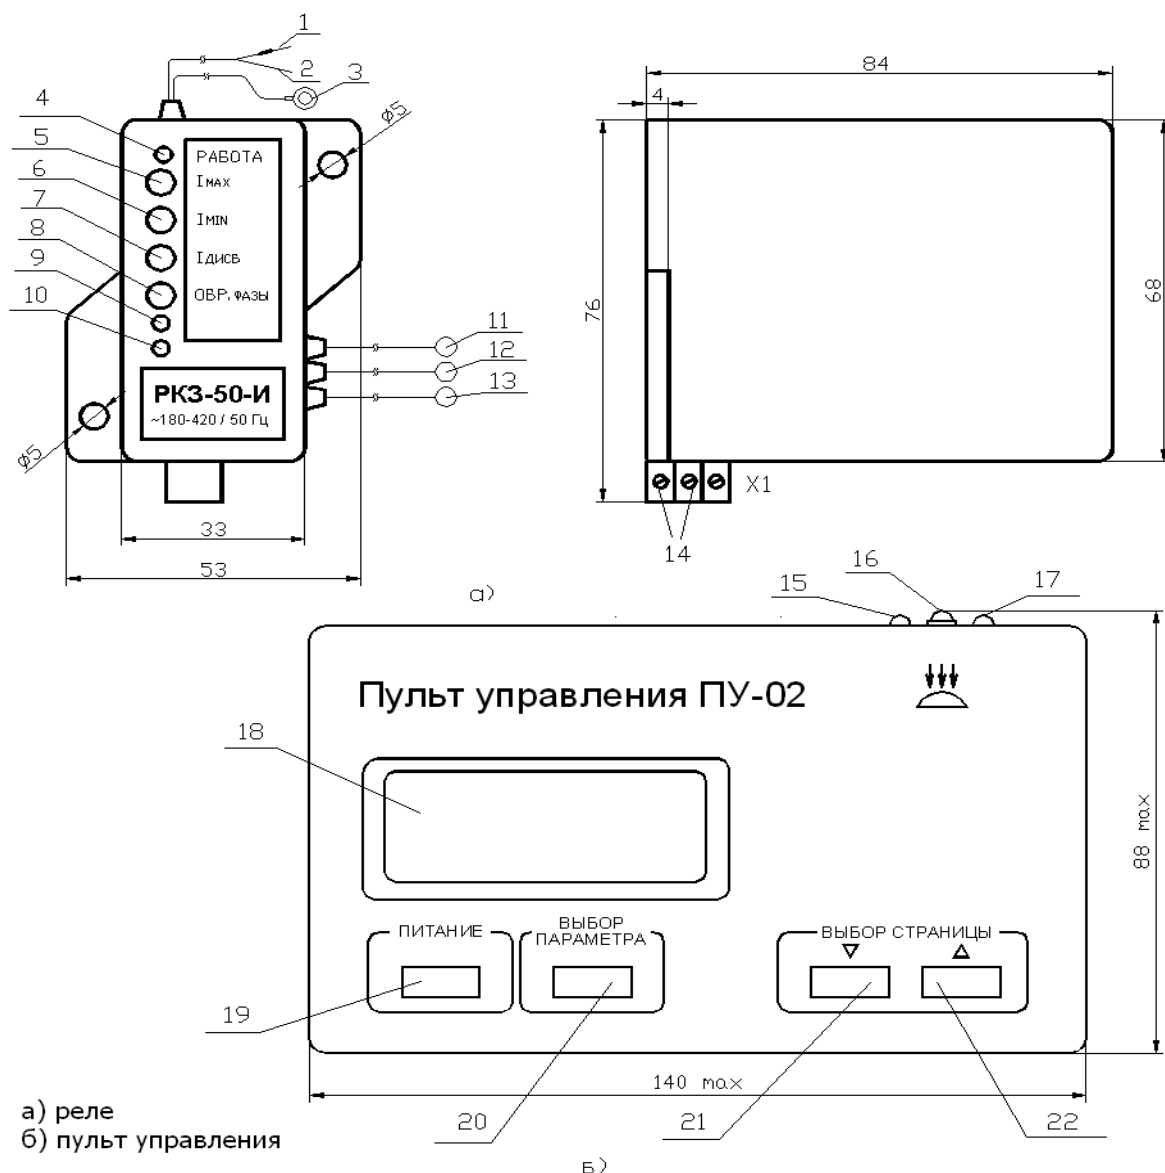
Внешний вид и габаритные размеры блоков РКЗ и ПУ-02
